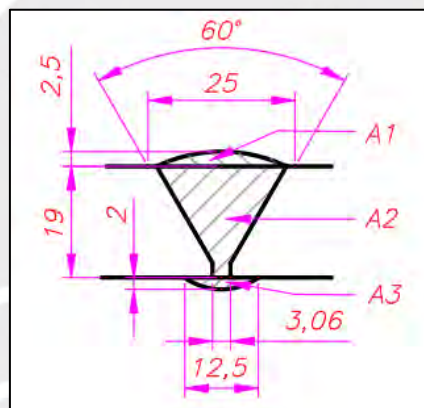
Esquema de cordón de soldadura generado con ambos procesos de soldadura
